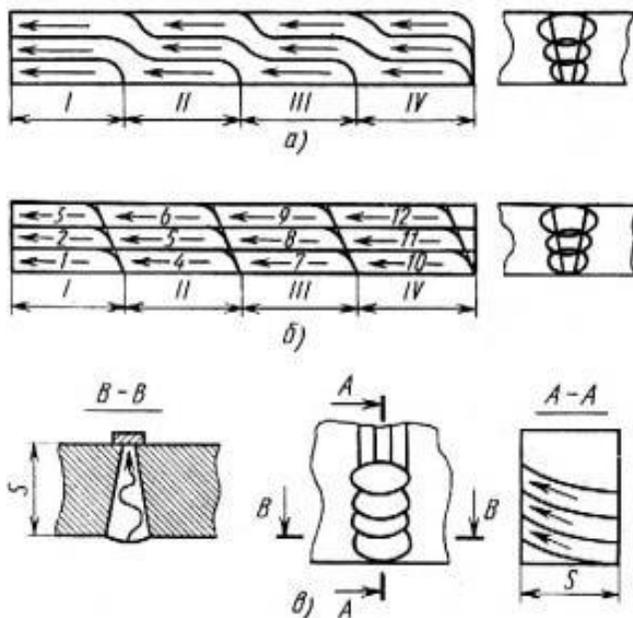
Схемы заполнения шва при сварке:
